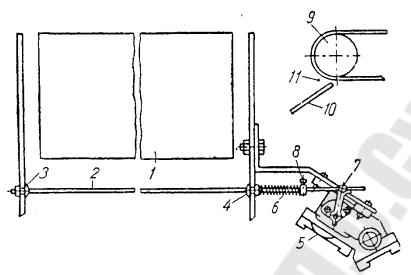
Предохранительное устройство со струной: 1 — барабан; 2 — проволока (струна) диаметром 3,2 мм; 3 — припайка; 4 — болт с отверстием; 5 — выключатель; 6 — пружина, работающая на сжатие; 7 — зажимная втулка; 8 — зажимное кольцо; 9 — приводной барабан; 10 — желоб; 11 — струна
